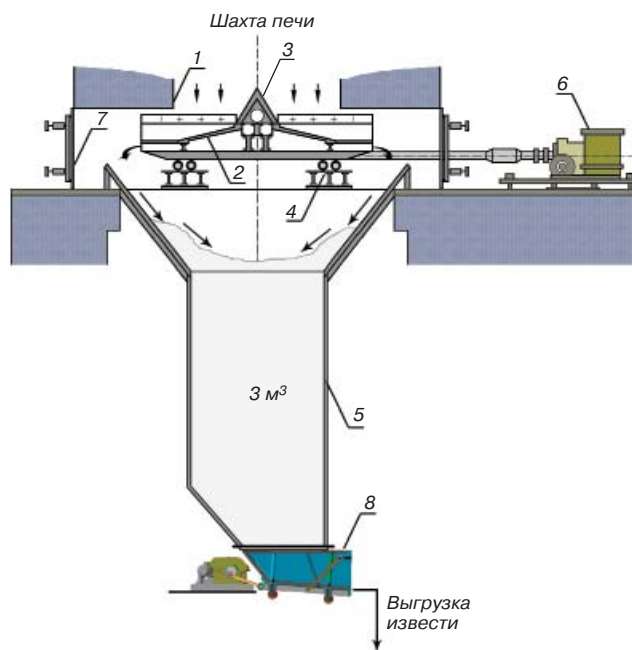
Выгрузочное устройство: 1 – шахта печи; 2 – колосниковая решетка; 3 – балка-рассекатель; 4 – катки; 5 – бункер извести; 6 – механический привод; 7 – смотровые люки
